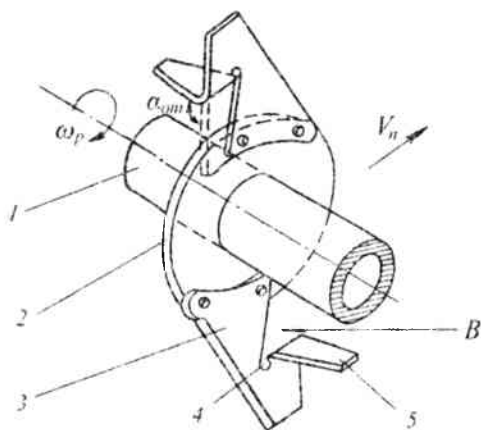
Ротационный рабочий орган с вырезными ножами для послойной обработки почвы: 1 – вал ротора; 2 – диски; 3 – основной прямой нож; 4 – окружное закругление выреза; 5 – дополнительный боковой нож
